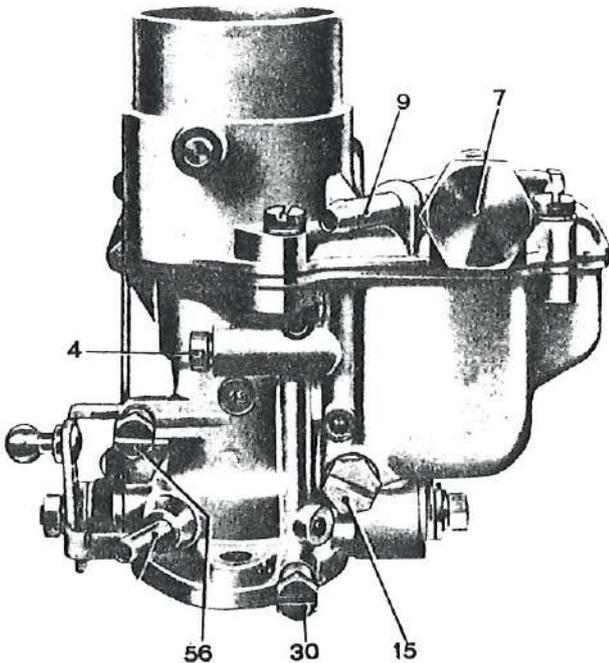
Carburador 28 ICP 6, lado entrada carburante, surtidores y tornillo regulación ralenti.
